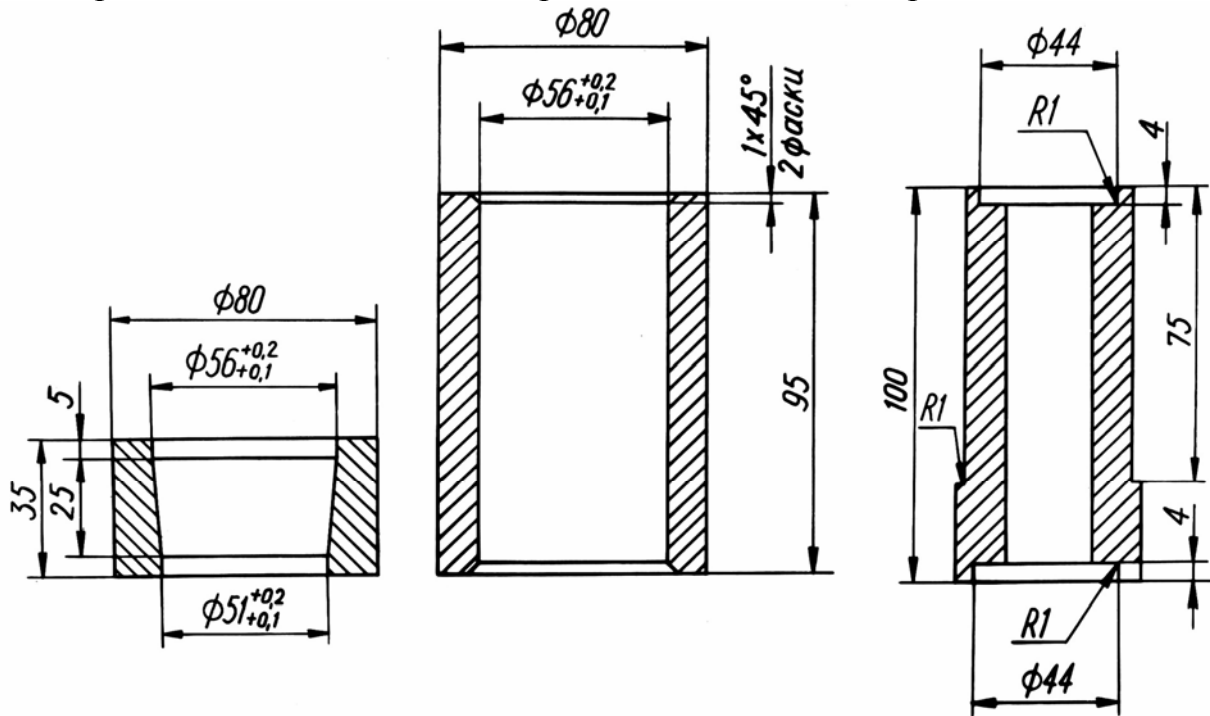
Оправки для запрессовки резинометаллических шарниров в ушко рессоры и кронштейны. Материал: сталь 40X, HRC 30-34
